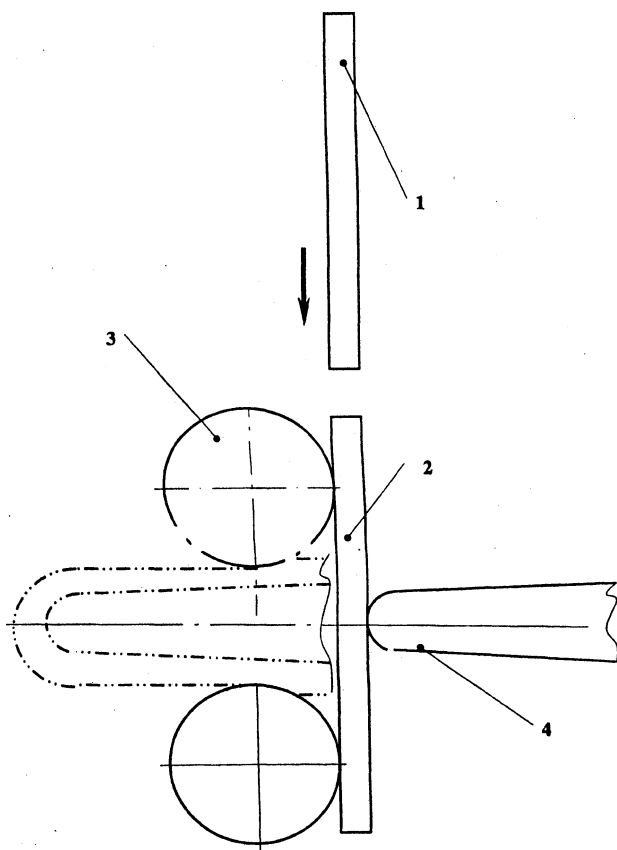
Схема прокатки заготовки переменной толщины на оправке
